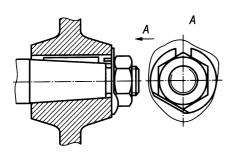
Крепление гайкой и отгибной шайбой с лапкой
